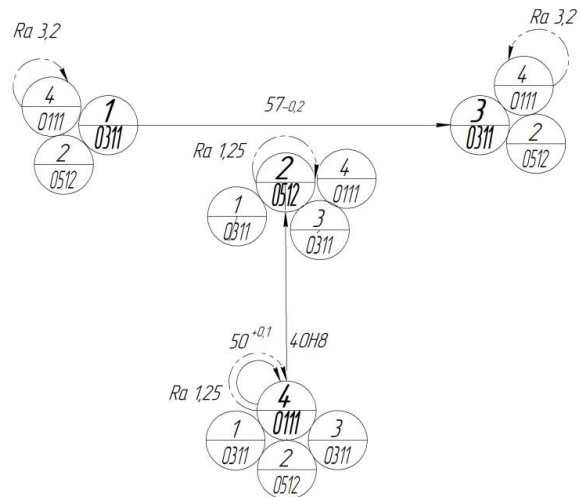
Граф размерных связей между элементарными поверхностями детали, насыщенный значениями шероховатости элементарных поверхностей
